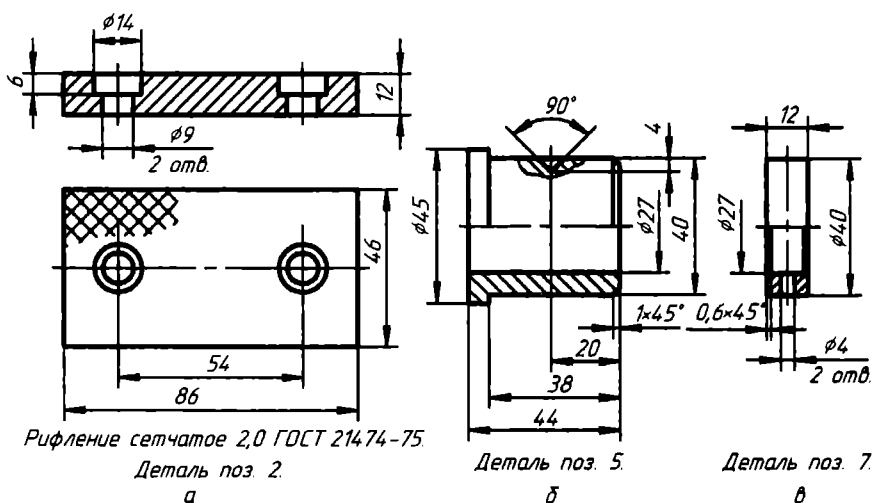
Чертежи: а — рабочей пластины; б — втулки; в — кольца
